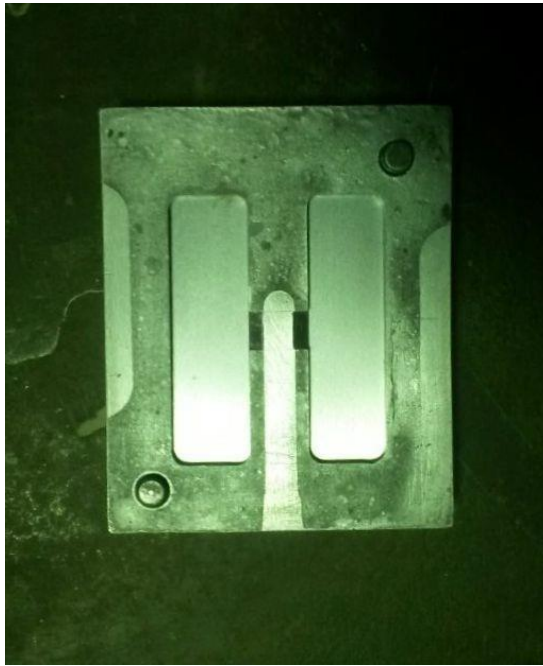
Зовнішній вигляд пресформи для виготовлення зразків
